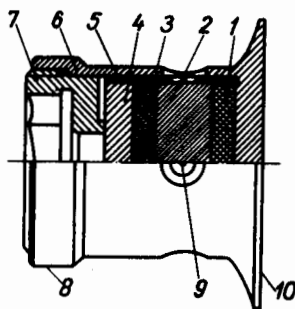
Составной ультразвуковой излучатель. 1 и 3 - пьезокерамические элементы; 2 и 4 - металлические шайбы; 5 - тефлоновый изолятор; 6 - корпус излучателя; 7 - армирующая гайка; 8 - узел крепления; 9 - клемма; 10 - излучающая поверхность.
